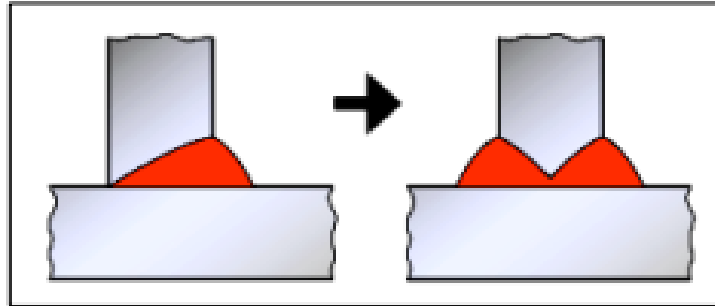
Configuration du Joint, les soudures à deux faces sont moins susceptibles.
